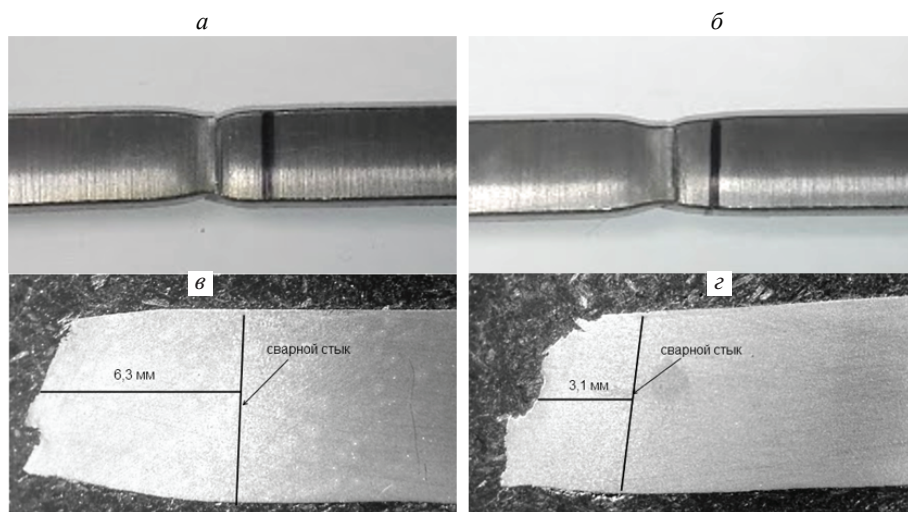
Фотографии образцов сварных соединений после испытаний на статическое растяжение:
